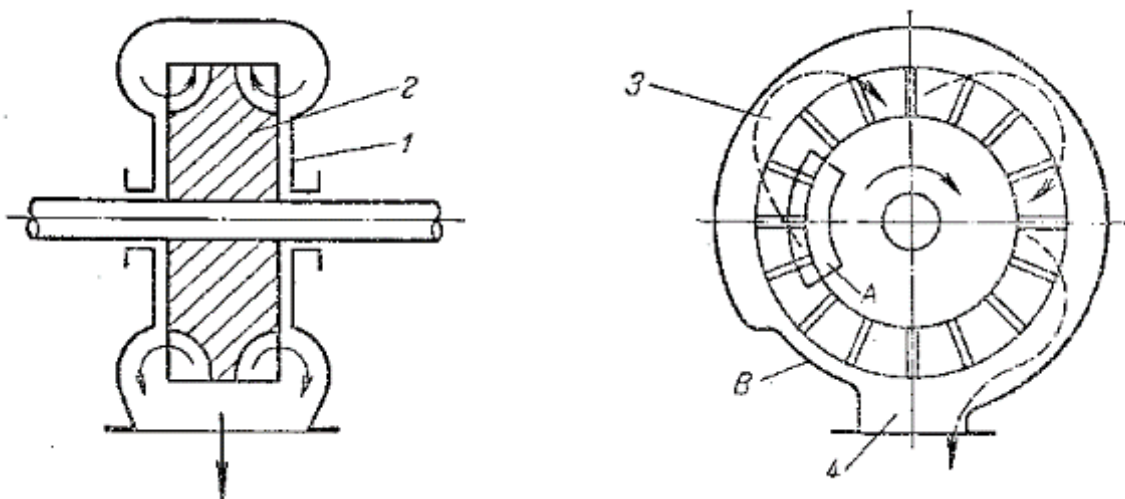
Вільновихровий насос: 1 – корпус; 2 – робоче колесо; 3 – кільцевий канал; 4 – нагнітальний патрубок
